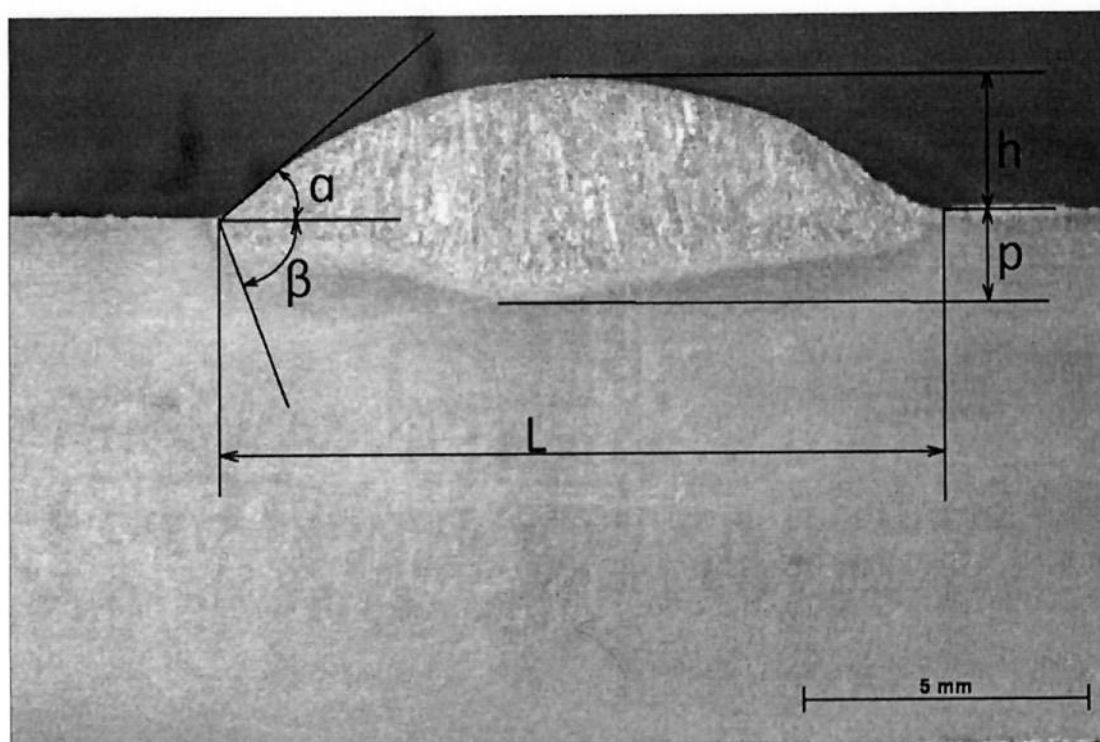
Macrografia do cordão sobre chapa com indicando as dimensões e ângulos.
